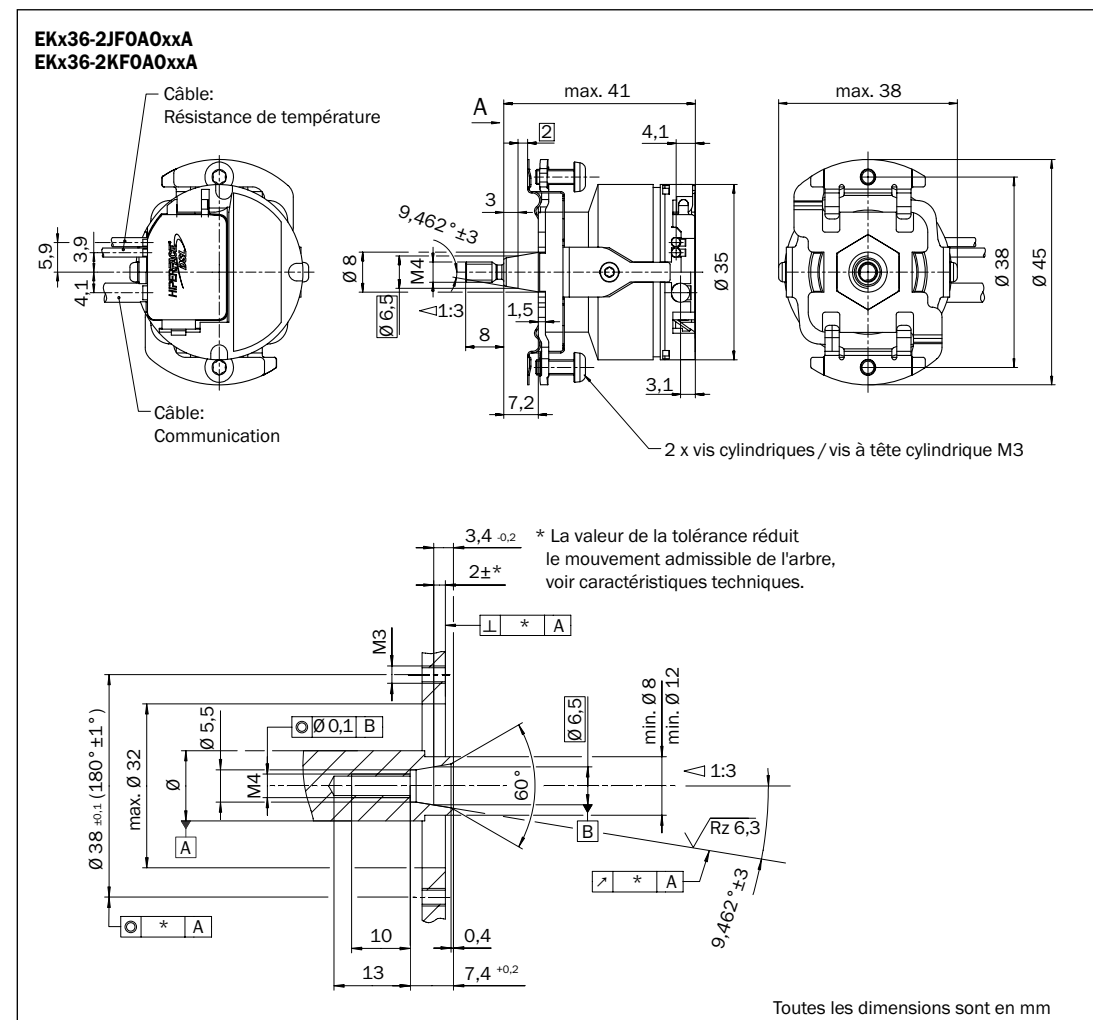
Plan coté et proposition de montage EKS36-2 / EKM36-2 arbre conique
